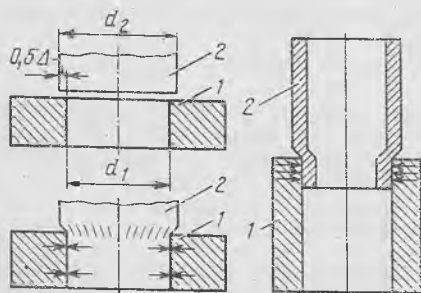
Последовательность схем соединений с нагревом охватываемой (1) или охлаждением охватываемой (2) детали
